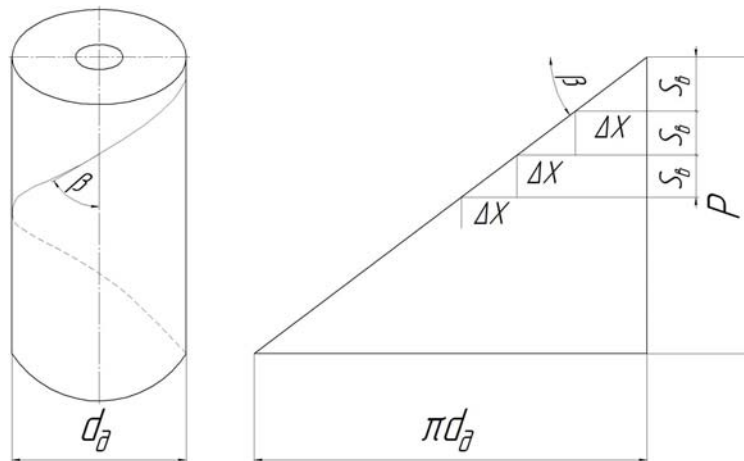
Перемещение фрезы относительно заготовки при нарезании косозубого колеса
